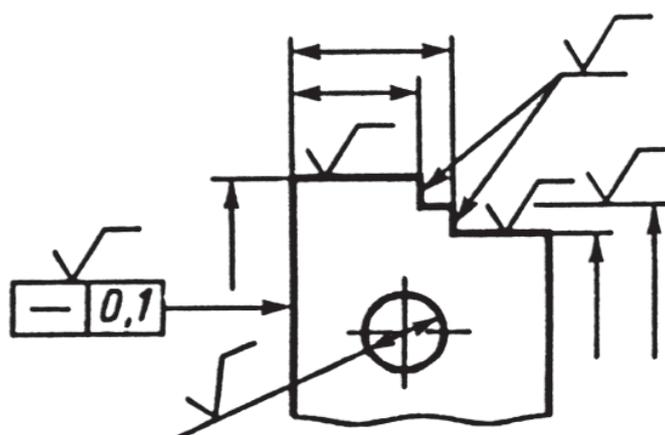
Расположение знаков обозначения шероховатости поверхности
